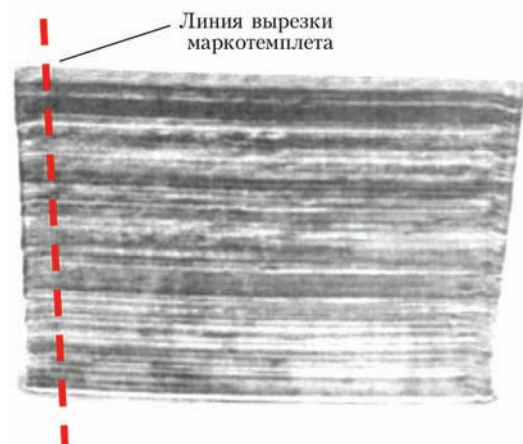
Схема вырезки макротемплета из наплавленной пластины
